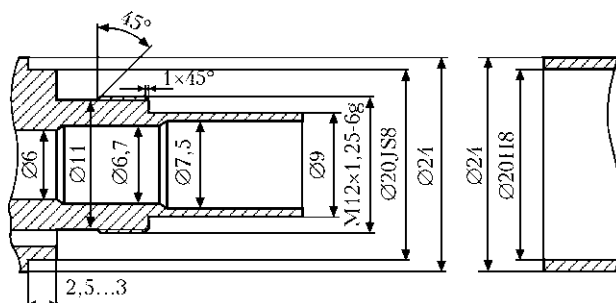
Схема подготовки соединения элементов чехла КНИ (шов № 3) под сварку GTAW
